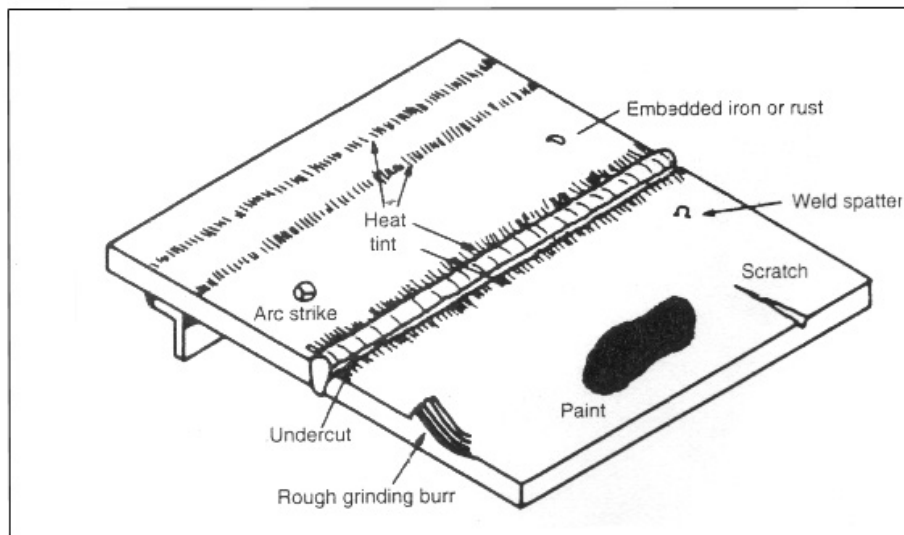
Tipos de defeitos superficiais que surgem durante a fabricação.
